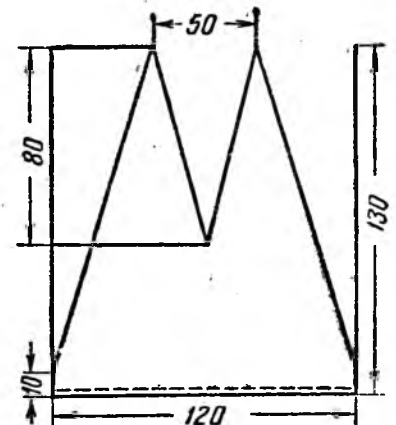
Выкройка носовой и кормовой части корпуса лодки.
